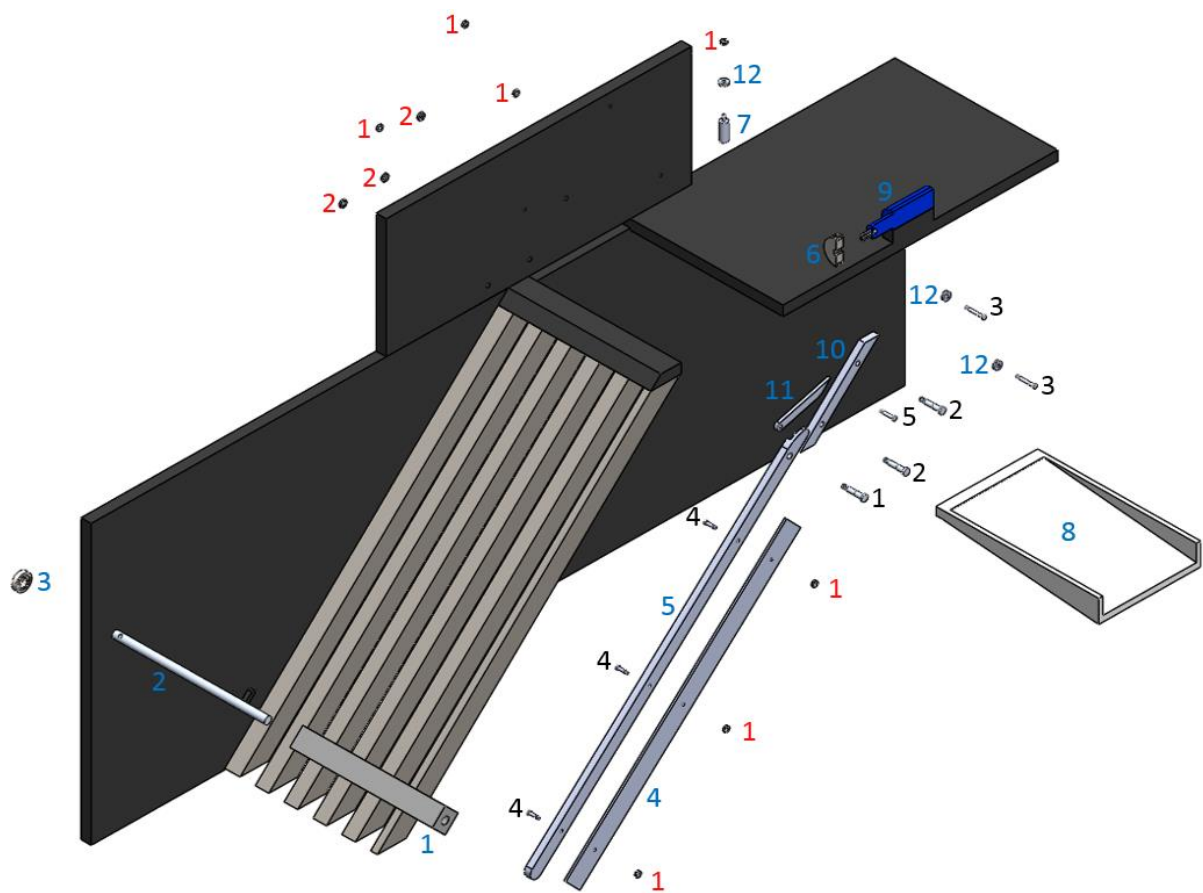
Vista explodida do mecanismo (vista em corte)
